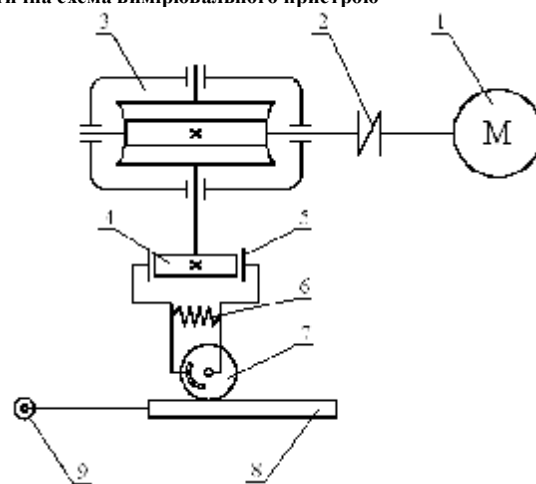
Кінематична схема вимірювального пристрою з системою для вимірювання динамічного натягу нитки:
